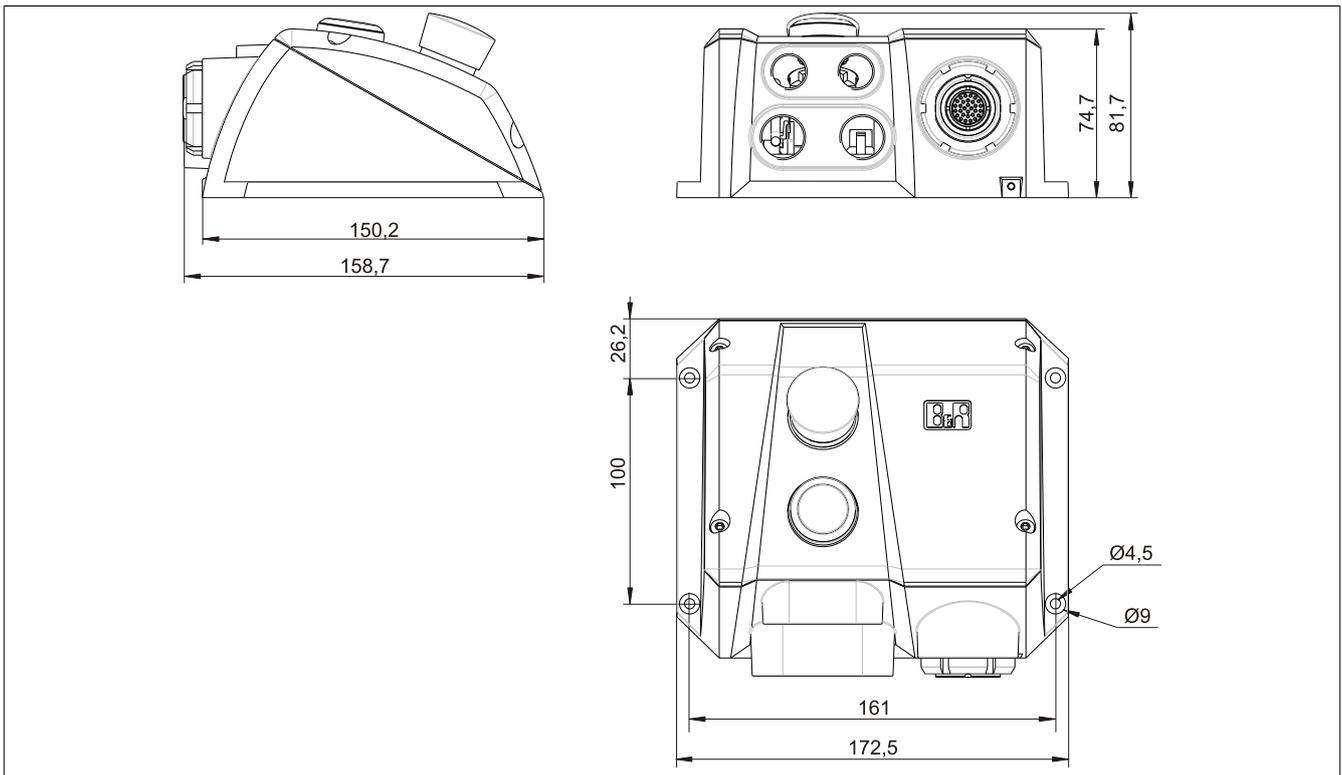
4MPCBX.0000-00 - Abmessungen
